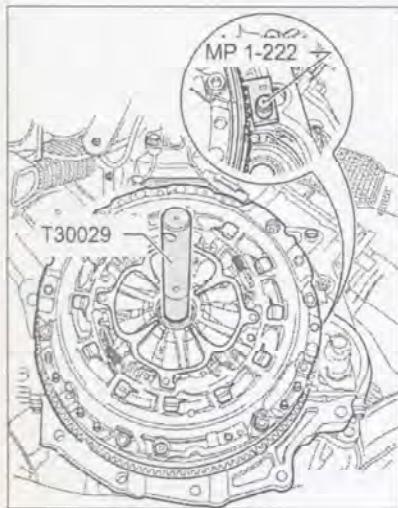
Установите центровочное приспособление T30029 и стопор MP 1-222.
